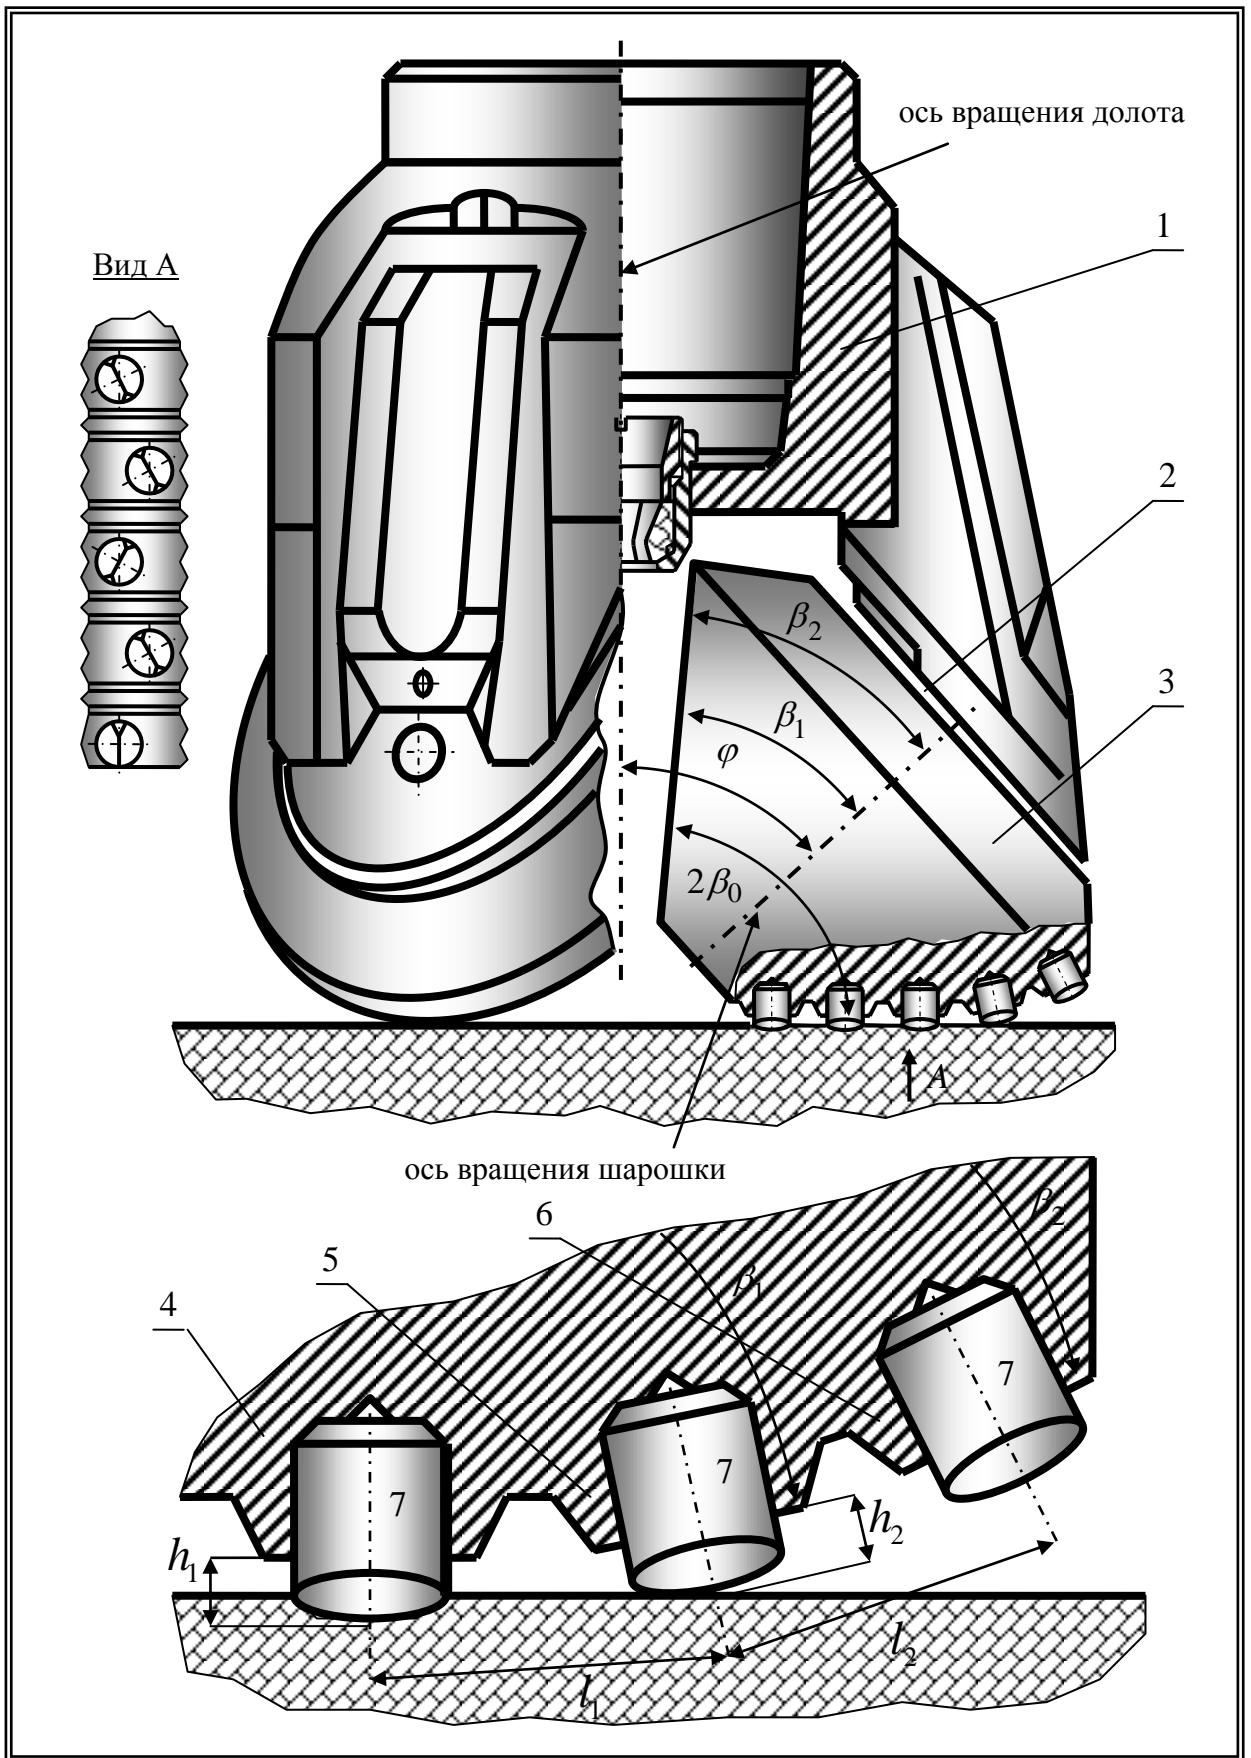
Схема шарошечного долота для твердых пород с разноориентированным зубчатым твердосплавным вооружением
